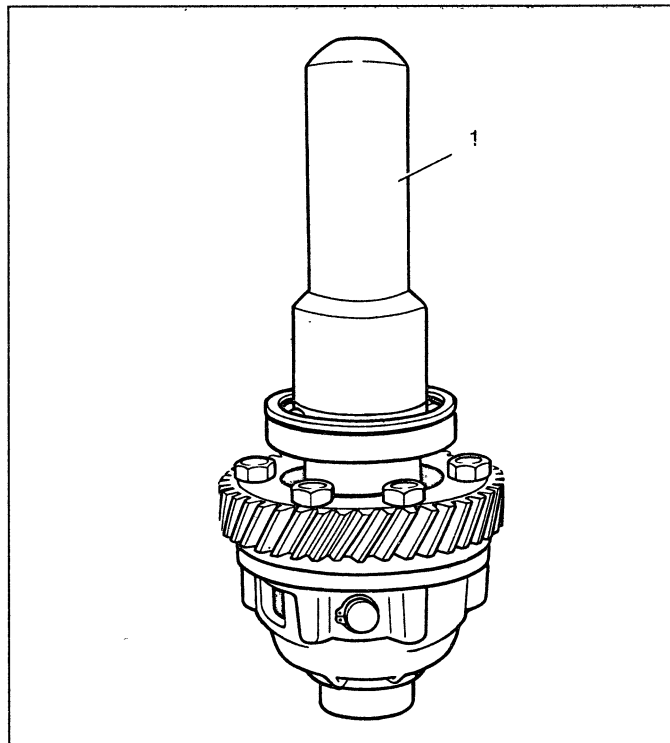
Напрессовка подшипника на корпус дифференциала: 1 – оправка 67.7853.9558
